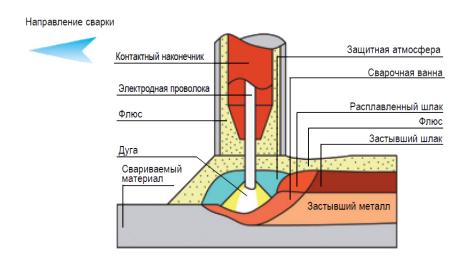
Технология автоматической сварки под флюсом
